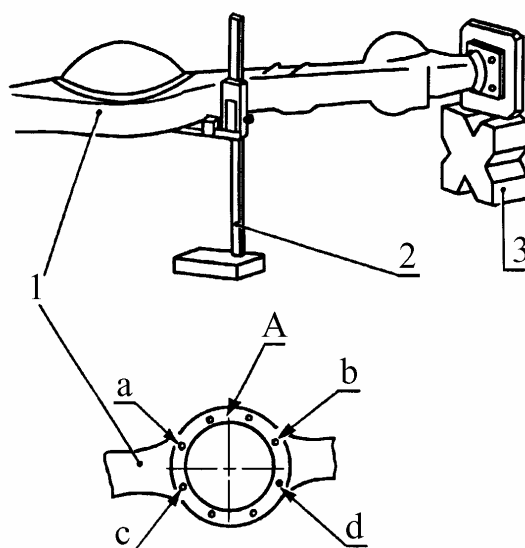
Проверка параллельности привалочной поверхности крепления редуктора:
